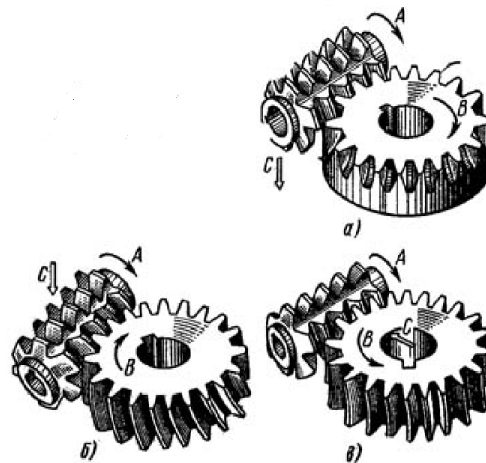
Схема нарізання коліс на зубофрезерних верстатах.
